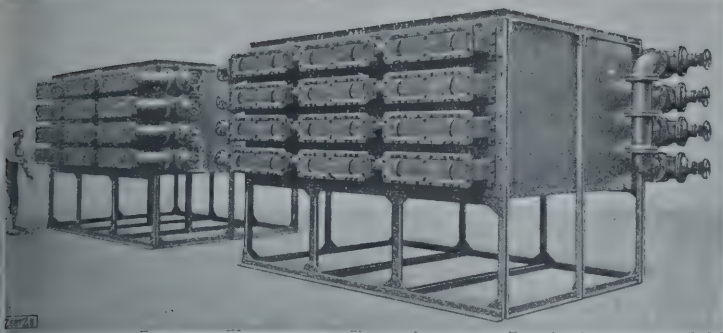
Luftkühler für die 44 000 kVA-Stromerzeuger mit einzeln ausziehbaren Teilkühlern
